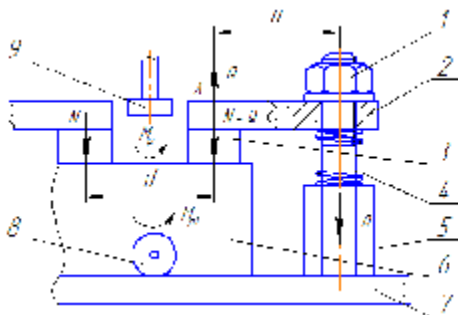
Кинематическая схема прихвата: 1 – гайка; 2 – рычаг; 3 – прижим; 4 – шпилька; 5 – стойка; 6 – заготовка; 7 – основание; 8, 9 – фрезы или сверла
